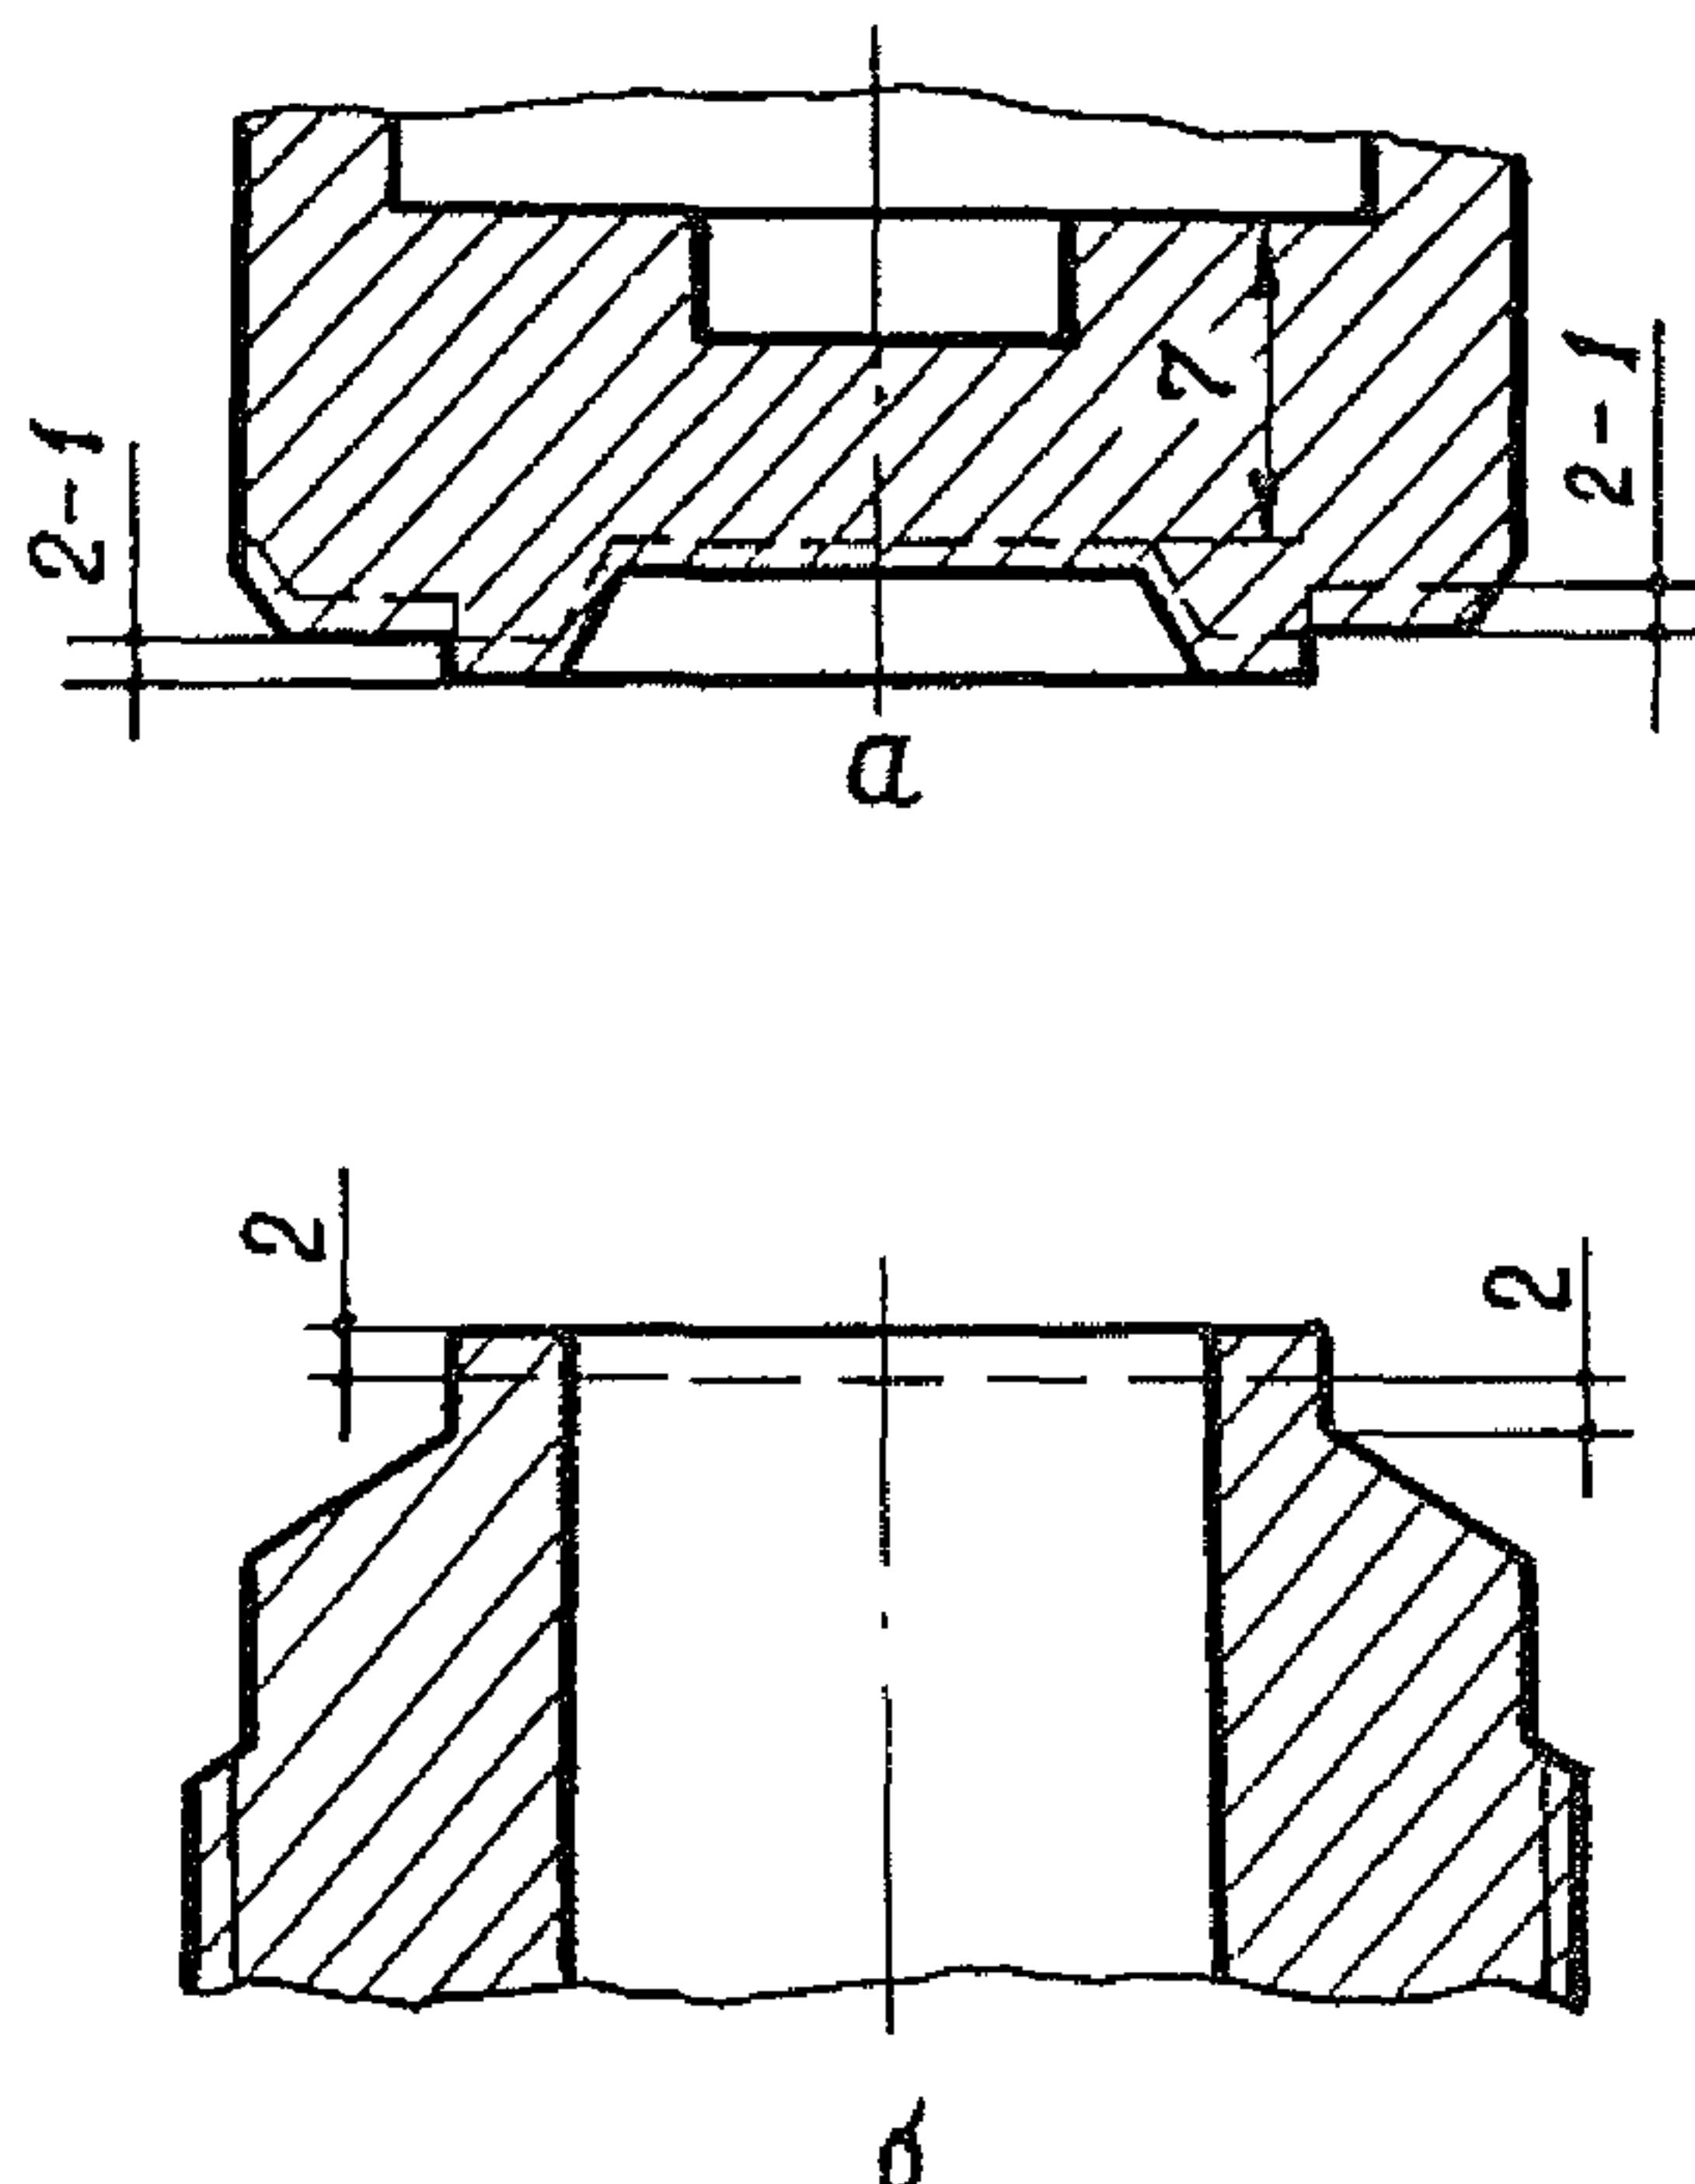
Ремонтные размеры уплотнительных поверхностей золотника (а) и сопла (б).
